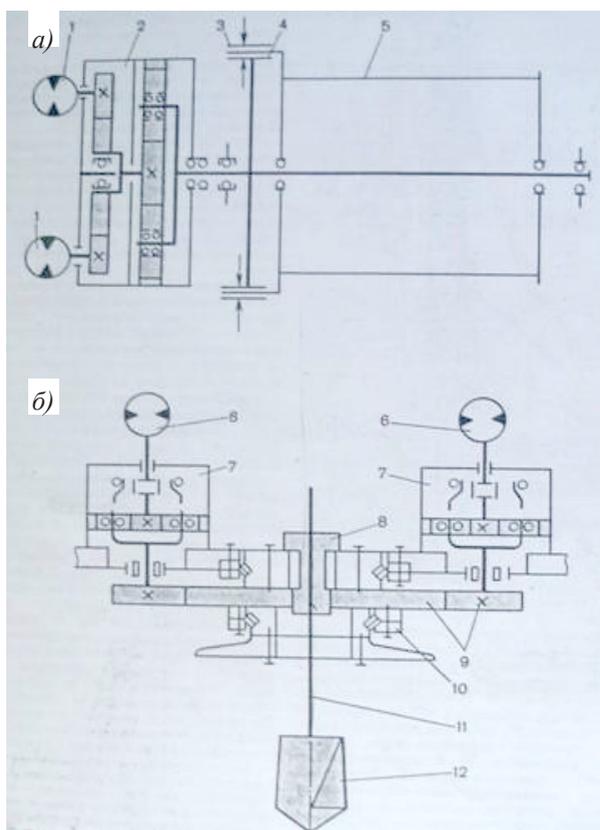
Схема привода бурильного оборудования ЭО-5123.50: а – общий вид; б – кинематическая схема
